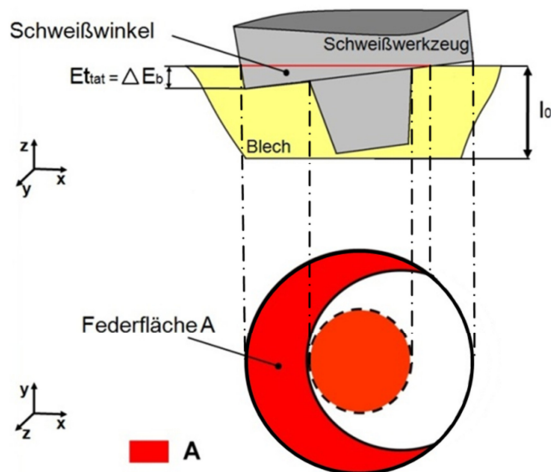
Federfläche A als Funktion der Werkzeuggeometrie und der Eintauchtiefe
